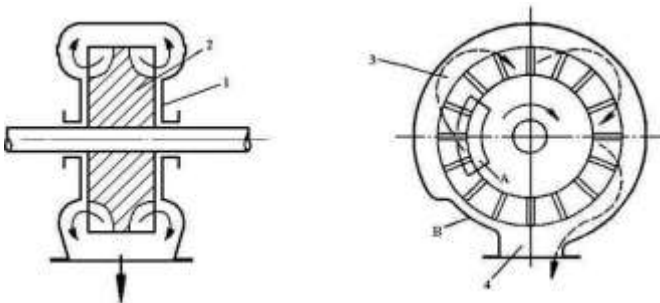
Схема вихрового насоса: А – вхідне вікно; В – ущільнююча ділянка; 1 – корпус; 2 – робоче колесо; 3 – кільцевий канал; 4 – нагнітальний патрубок
